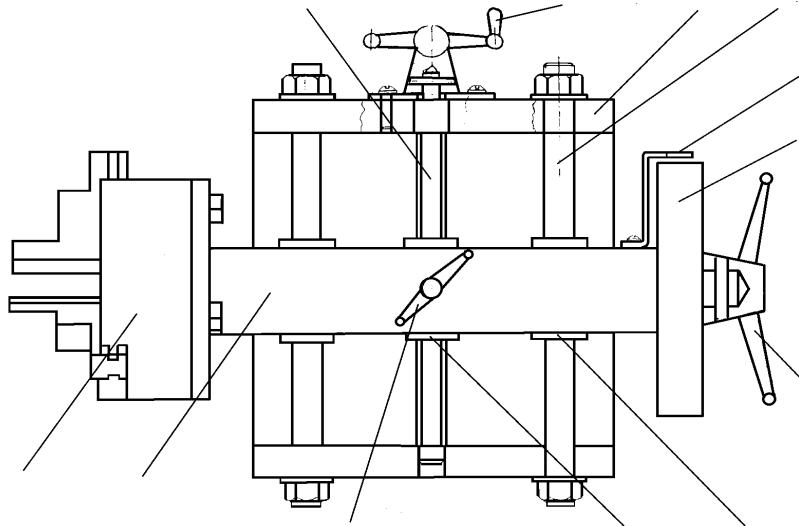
Пристосування призначене для точного фрезерування і фрезерування невеликих деталей на токарному верстаті.
